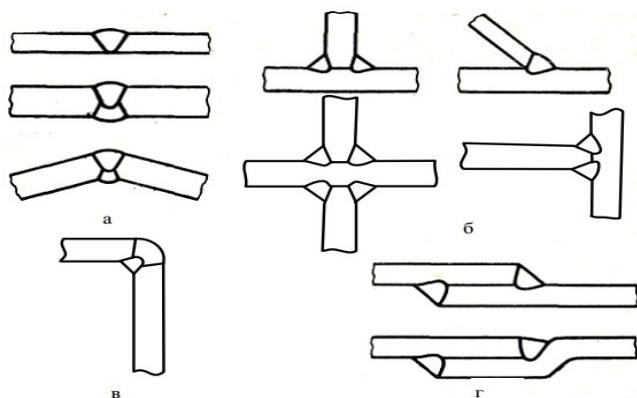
Основные типы сварных соединений: а - стыковые; б - тавровые; в - угловые; г – нахлесточные.
